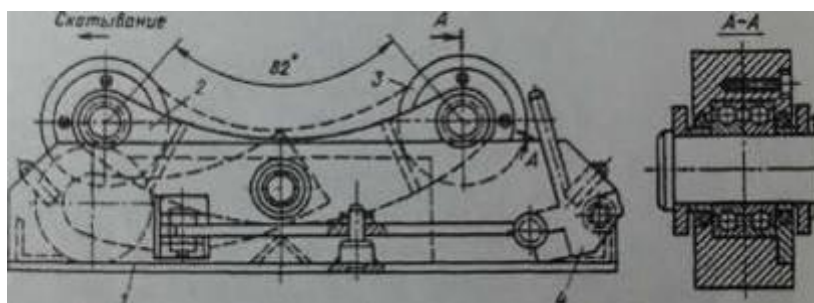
Роликовая опора типа ОР: 1 - корпус; 2 - обойма; 3 - ролик; 4 - стопорное устройство
